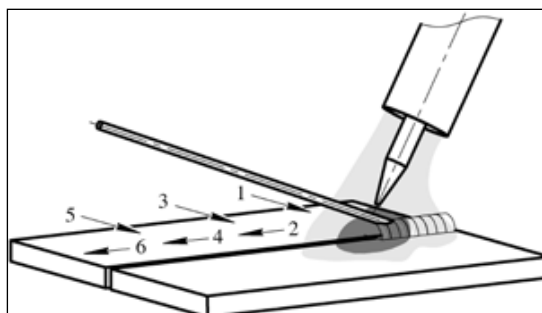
Пример манипуляции присадочной проволокой при TIG сварке
